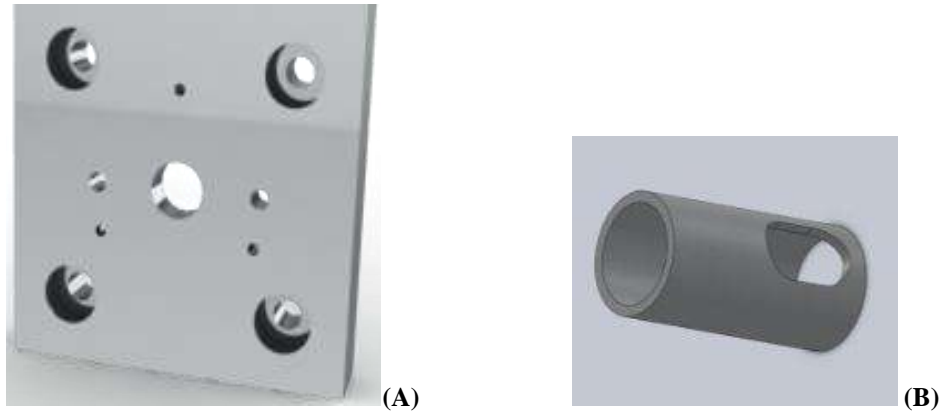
(A) Placa de montaje y (B) cilindro de acoplamiento para el encoder.
